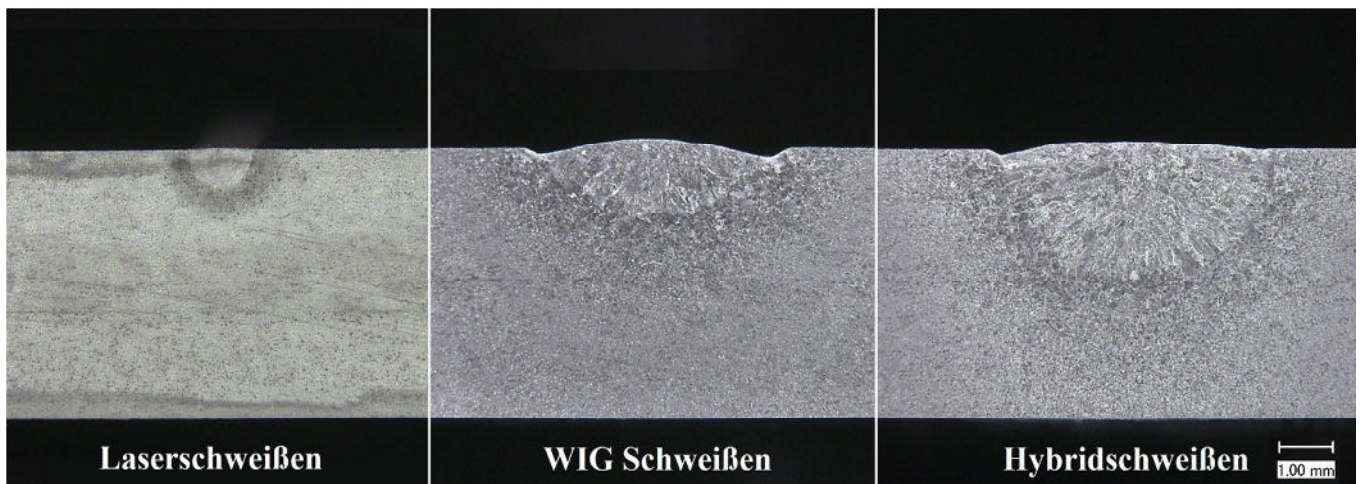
Makroschliffe der Querschnitte der Schweißnähte, die mit den entsprechenden Schweißparametern gemacht wurden. Die Analyse der Makroschliffe und die nachfolgende Berechnung zeigten die Steigerung des Energieanteils beim Hybridschweißen, der durch das Schweißen von Metall aufgesaugt wurde, und des Energieanteils, der für die Heizung und die Schmelzung des Schweißnahtmetalls gebraucht wurde, bezüglich der Energie, die von der Schweißwärmequellen hergestellt wurde. Auch wurde eine Vergrößerung des Verhältnisses der Schweißtiefe zur Nahtbreite beim Hybridschweißen des Baustahls S-235JR mit den entsprechenden Schweißparametern bemerkt.
